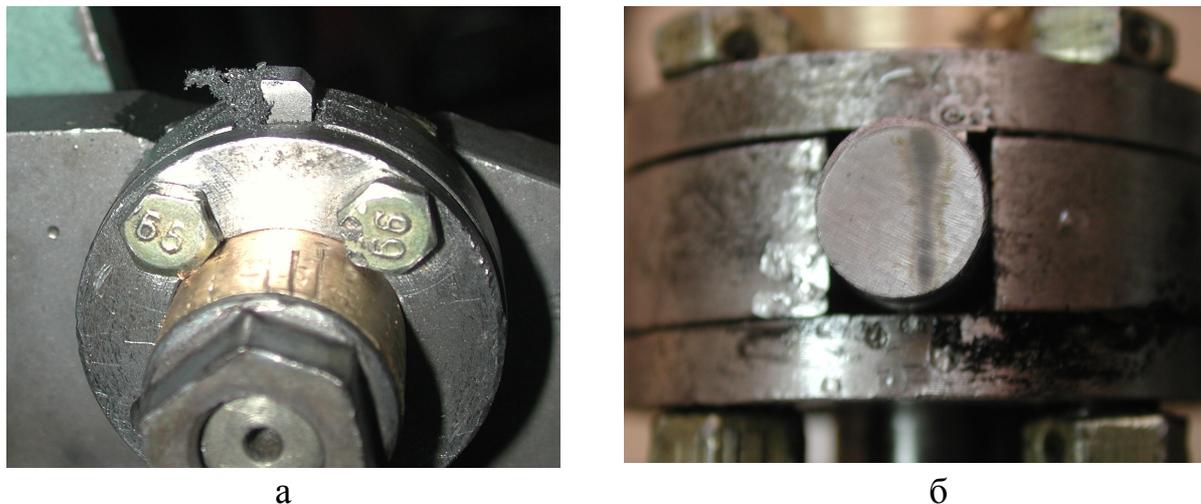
Поверхность образца после проведения испытаний: а – твердый сплав (вид с боку); б – быстрорежущий образец (вид с торца образца)
